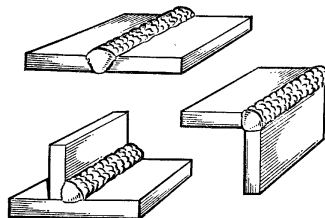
Вид нормальных швов, выполненных газовой сваркой
